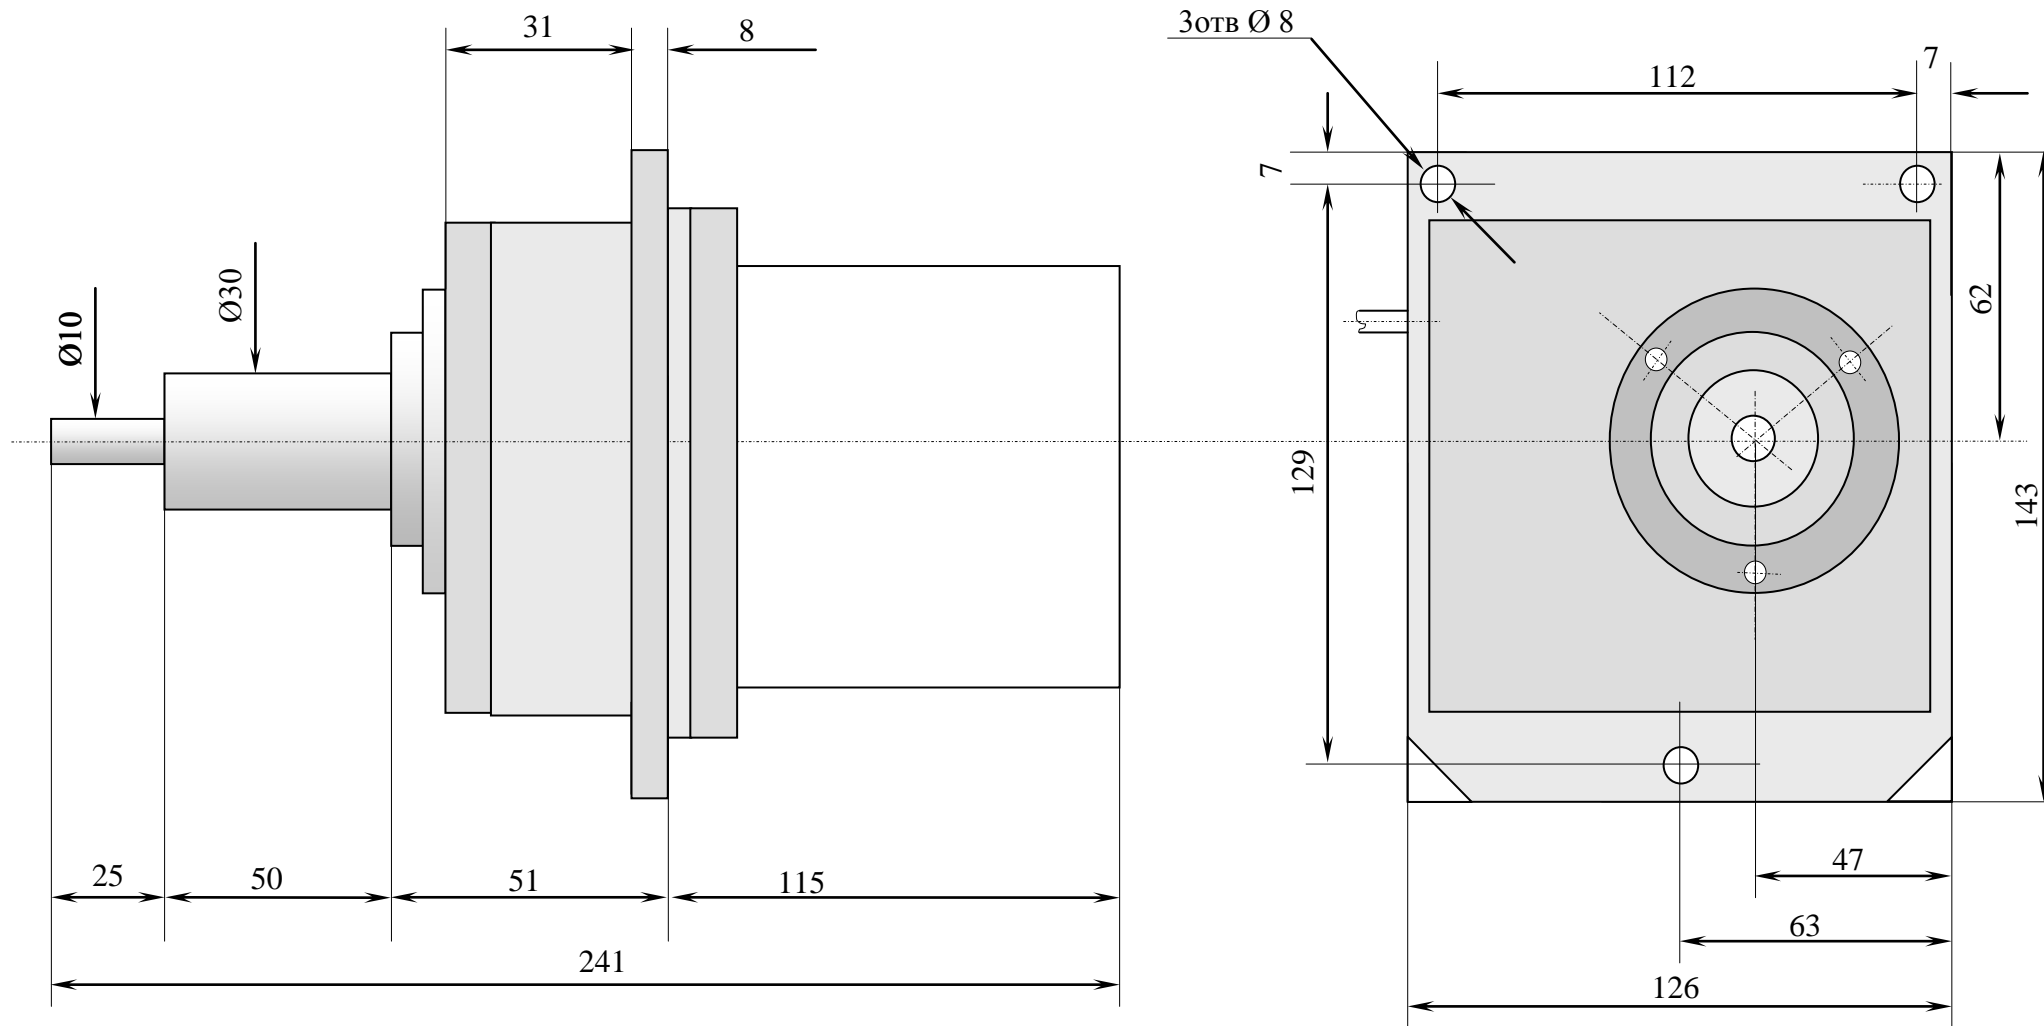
Габаритные и присоединительные размеры часового механизма мод. ЧМ-3
